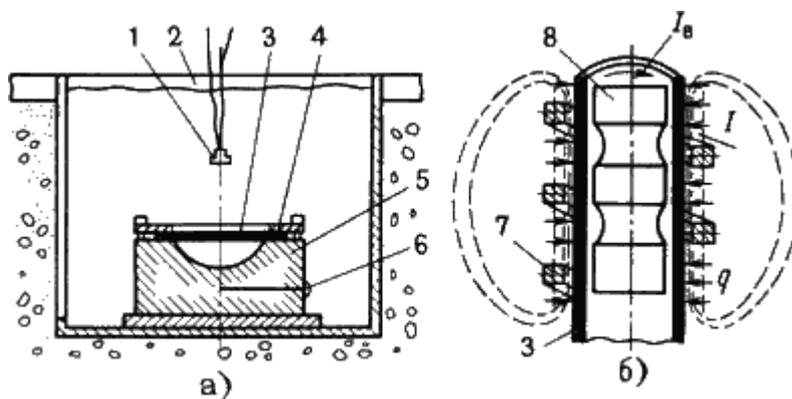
а) - штамповка взрывом; б) – электромагнитная штамповка
